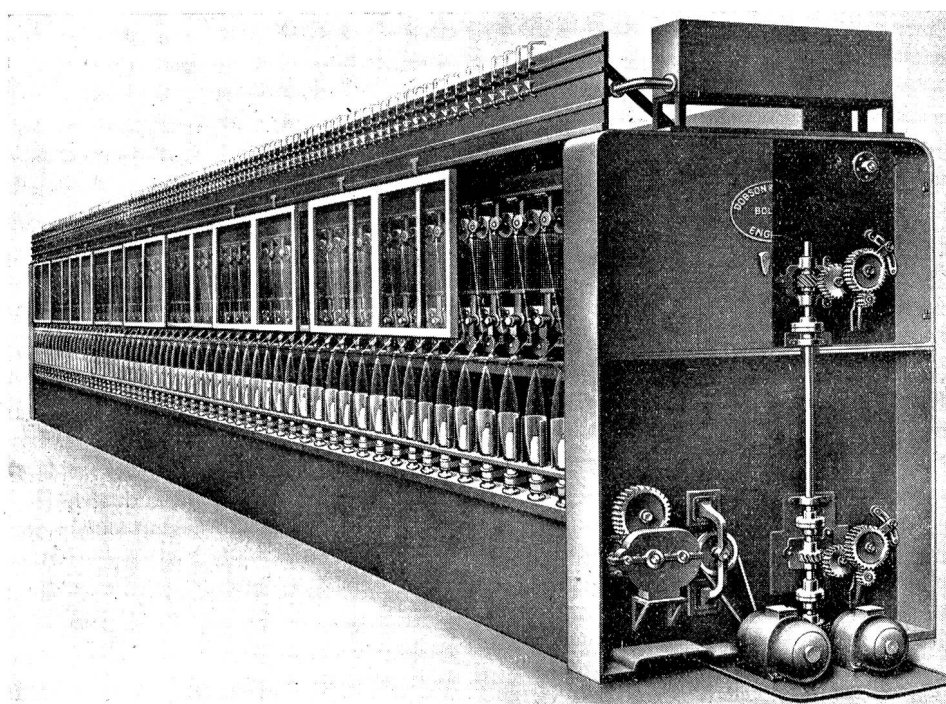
„Nelson“-Rayonspinnmaschine. Ansicht der „trockenen“ Seite
